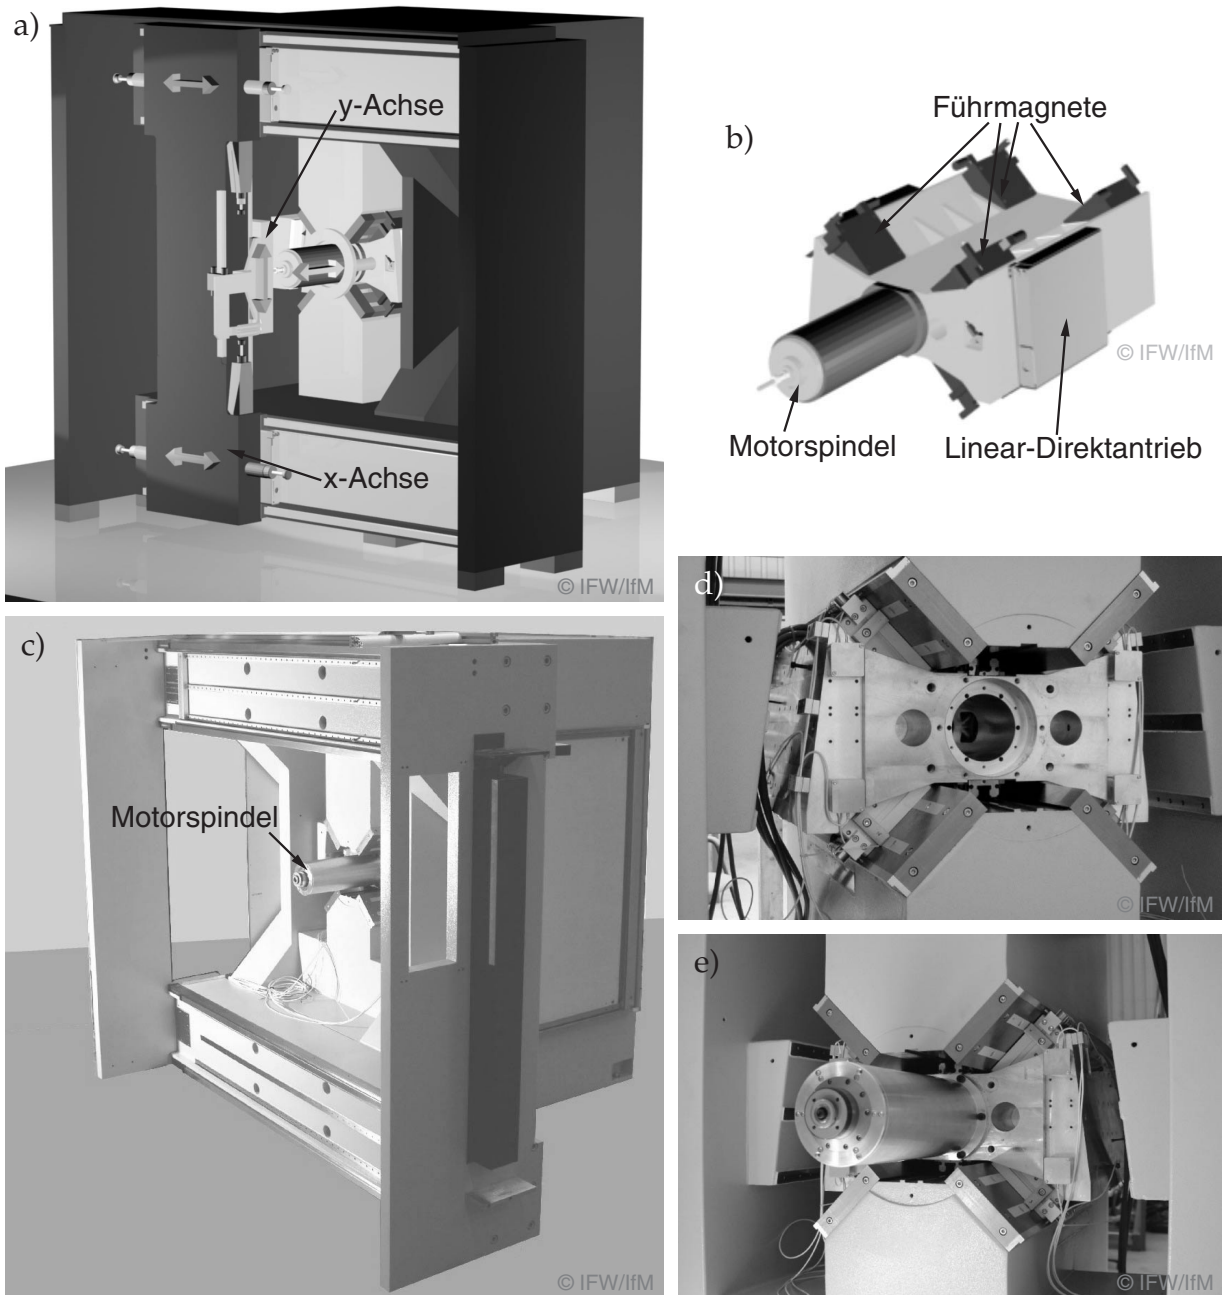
Ansichten der SCHNELLEN MASCHINE: a) CAD-Modell der gesamten Maschine; b) CAD-Modell der z-Achse; c) Ansicht der Maschine während des Aufbaus; d), e) Ansicht der z-Achse vor und nach der Montage der Motorspindel
